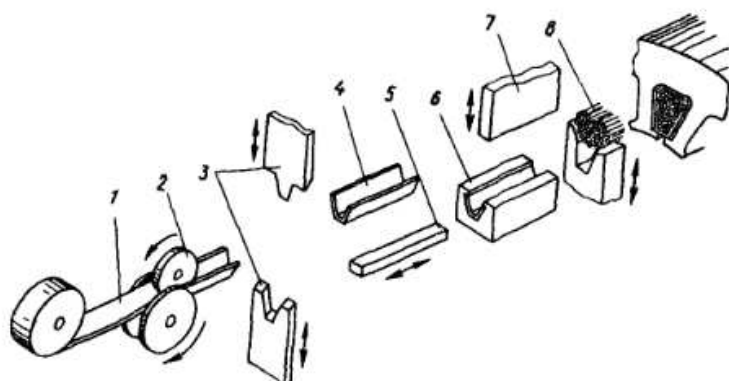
Схема работы станка для заклинивания пазов статора (пазовые клинья из узкой ленты)
